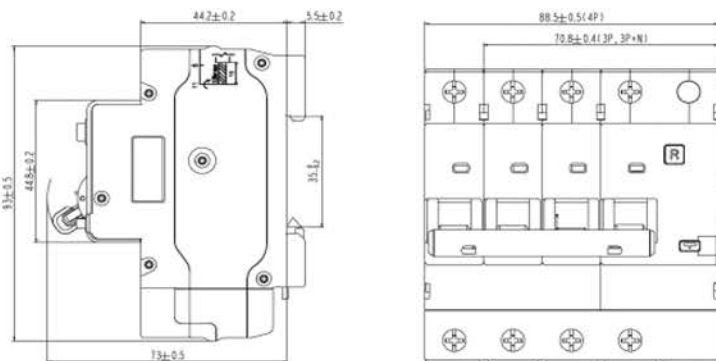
Установочные и габаритные размеры ДИФ-103 6кА 3P, 3P+N
